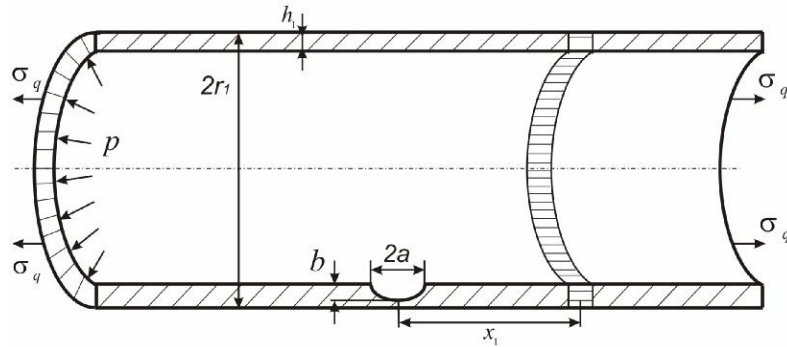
Схема навантаження зварного з'єднання трубопроводу з тріщиною
